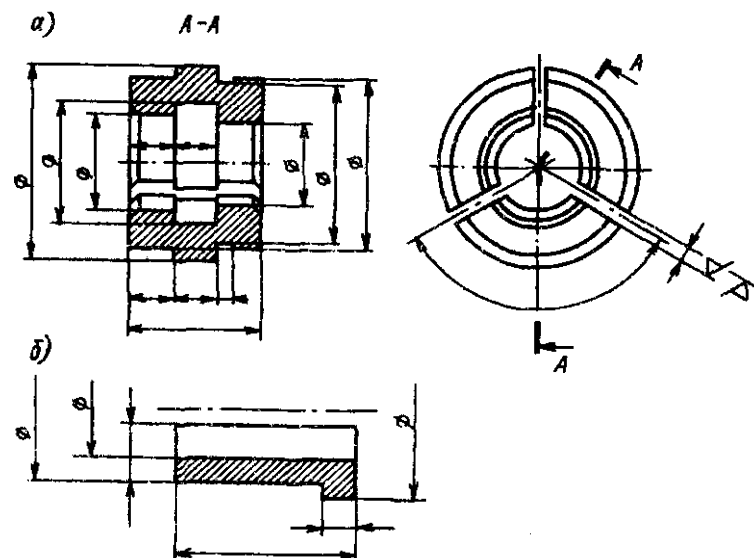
Деталь, получаемая разрезкой заготовки: а — невзаимозаменяемая; б — взаимозаменяемая
